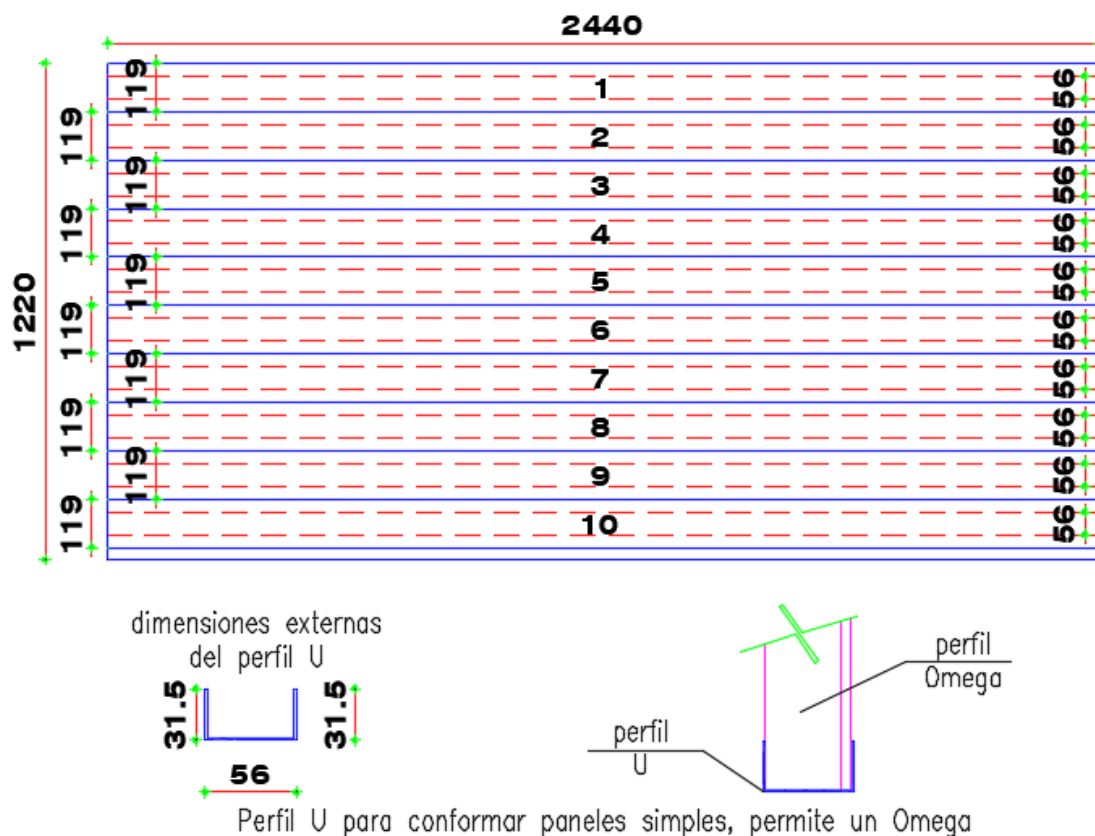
Plancha de Acero galvanizado con dimensiones para corte y doblado
